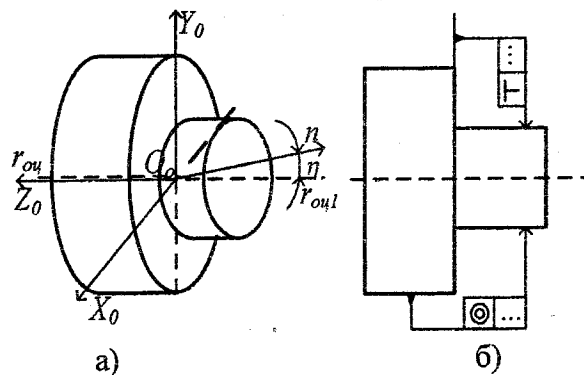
Обрабатываемая на токарном станке деталь: а - общий вид обрабатываемой детали; б - рассматриваемые погрешности расположения
